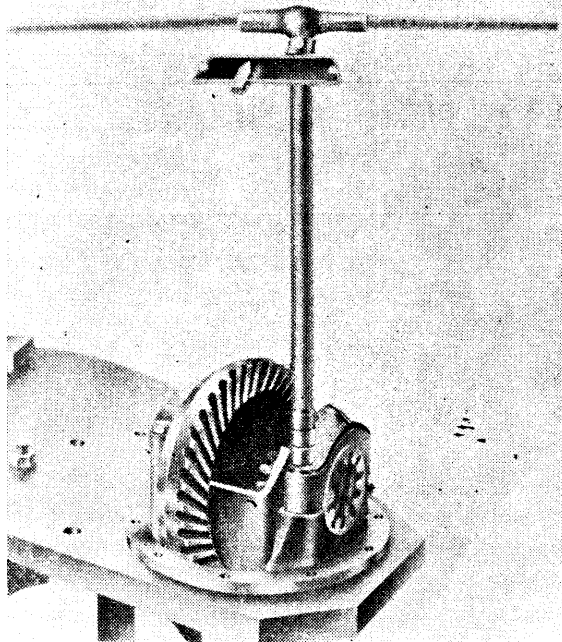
Vorrichtung zum Auflegen des Ausgleichgetriebes, P. 36.
